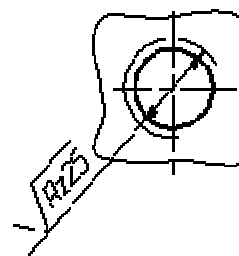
Пример обозначения шероховатости внутренней резьбы
